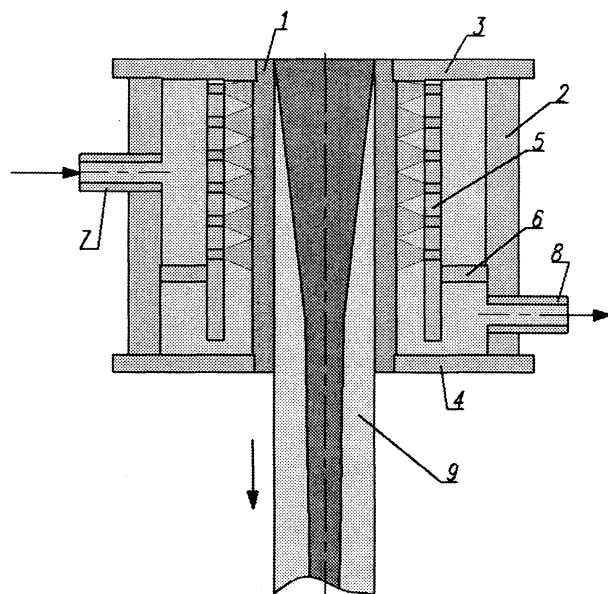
Схема струйного кристаллизатора: 1 – гильза; 2 – корпус; 3 – верхний фланец; 4 – нижний фланец; 5 – экран; 6 – перегородка; 7 – подводящий патрубок; 8 – отводящий патрубок; 9 – слиток
